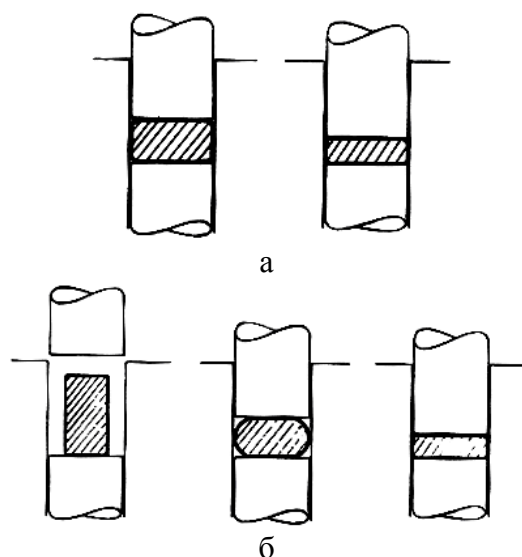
Схемы закрытой штамповки пористых заготовок:
